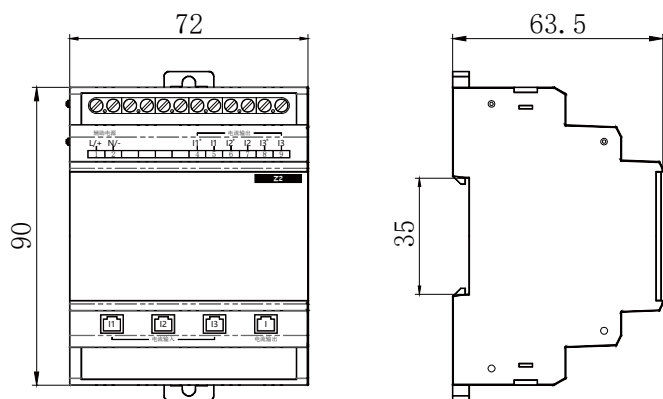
Внешний вид и габаритные размеры модуля коммутации Z2
